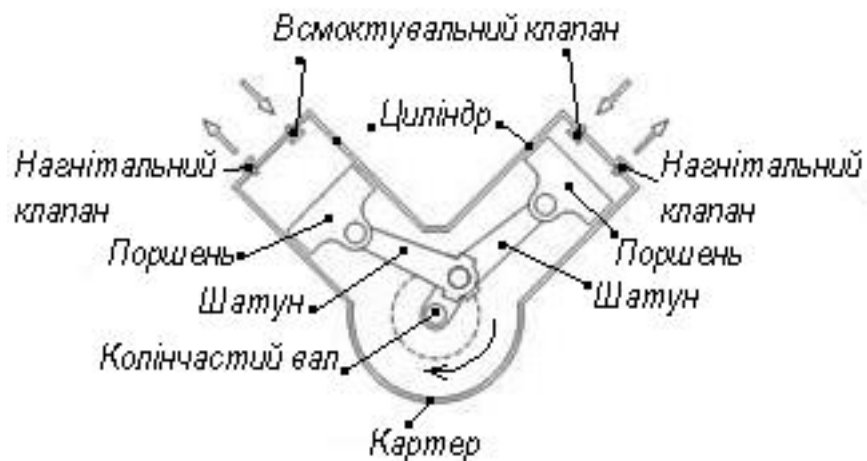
Принципова схема двоциліндрового V-подібного поршневого компресора
